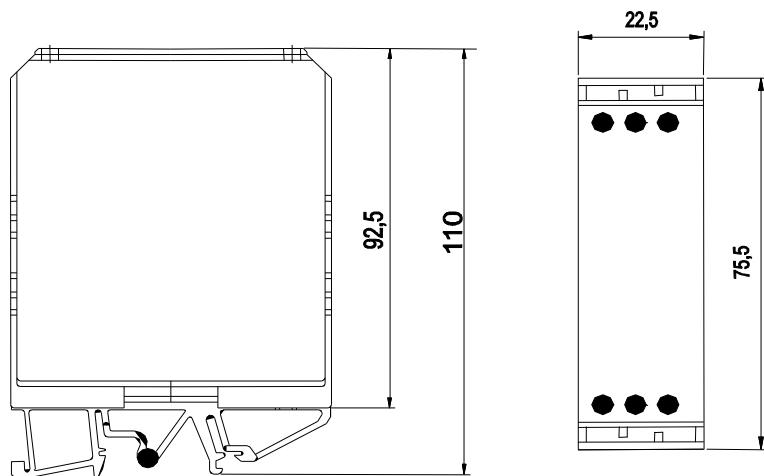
Dimensionamento para montagem (Cotas em milímetro)
